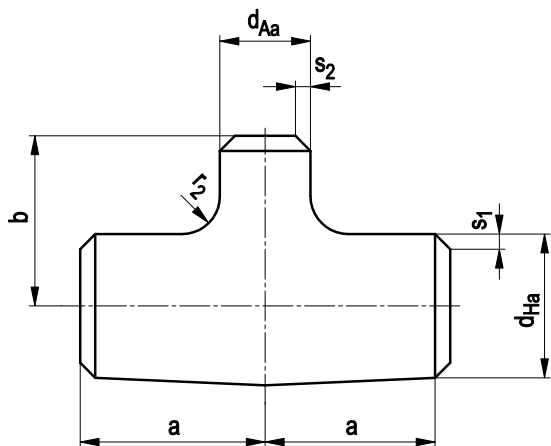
Gepresstes Einschweiß-T-Stück
